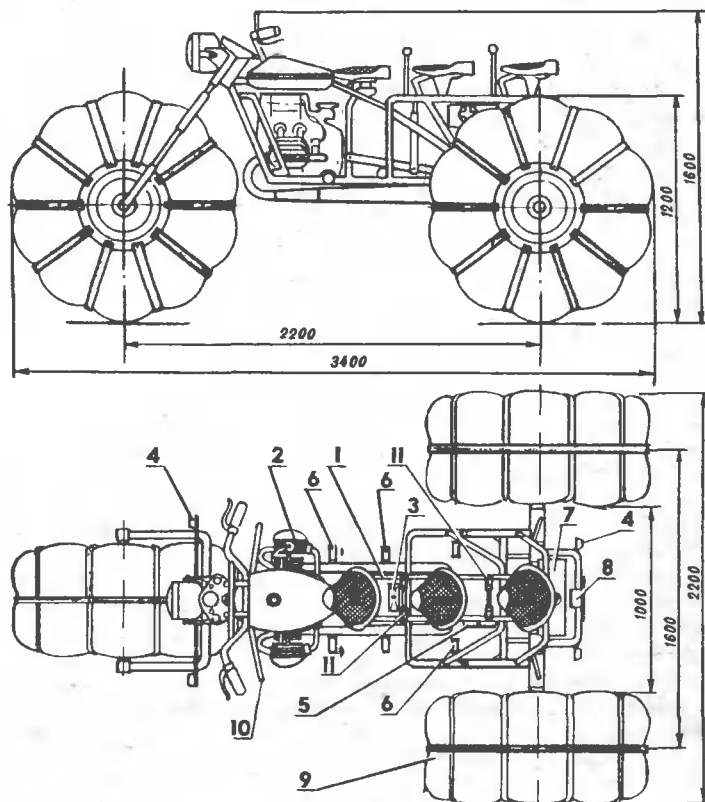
Пневмоход «Патруль» на базе мотоцикла «Урал»: 1 — рама пневмохода, 2 — двигатель, 3 — канистра для масла, 4 — указатели поворота, 5 — аптечка, 6 — подножки водителя и пассажиров, 7 — дополнительный топливный бак, 8 — стоп-сигнал, 9 — колеса, 10 — дуги безопасности, 11 — опорные рукоятки пассажиров.
